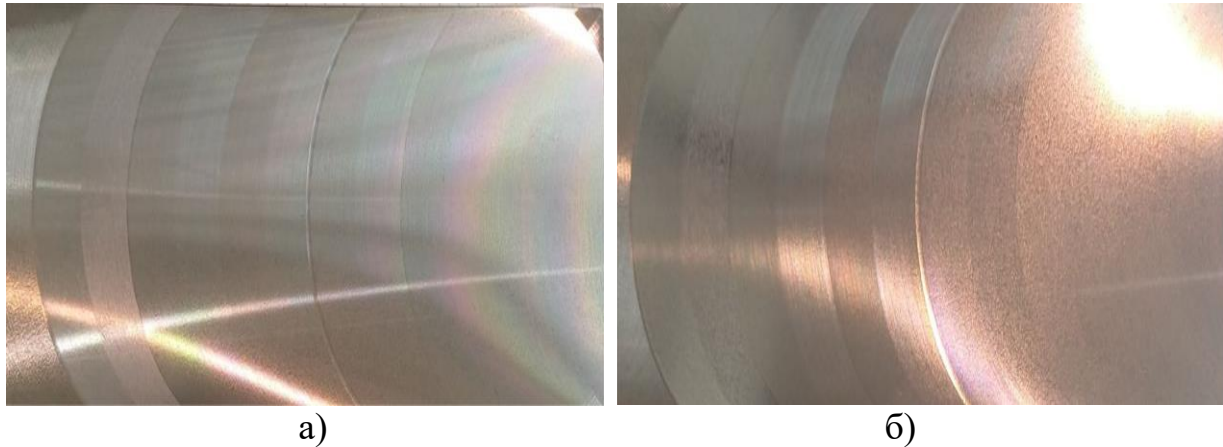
Зображення оброблених поверхонь заготовок з ЧВГ після фінішного фрезерування: а) КНБ та б) НК
